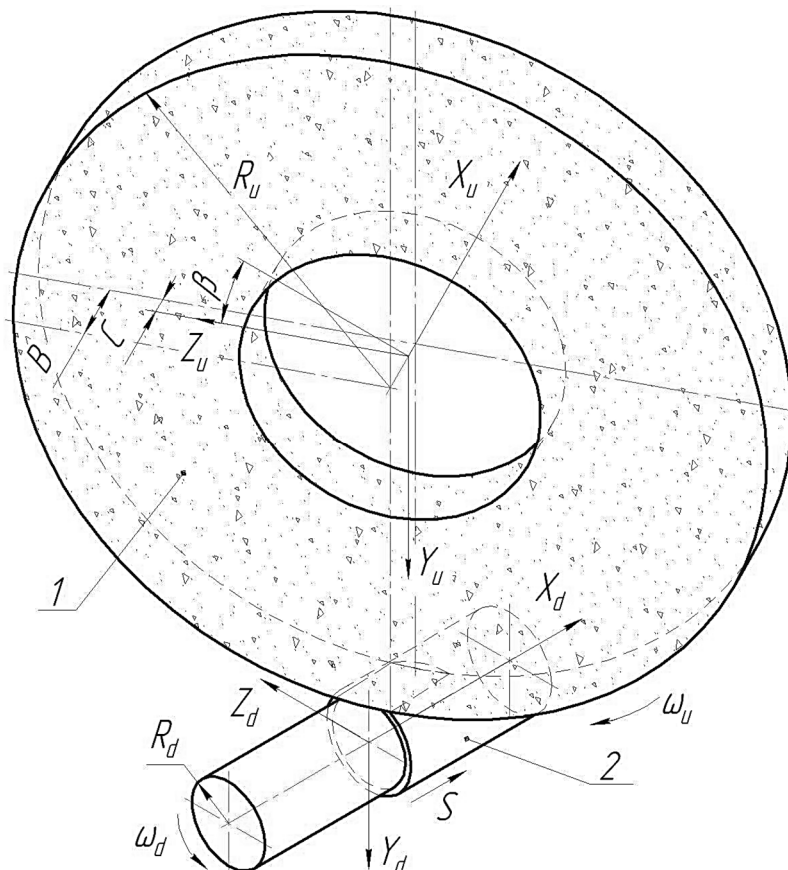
Схема однопрохідного чистового шліфування циліндричної поверхні вала
